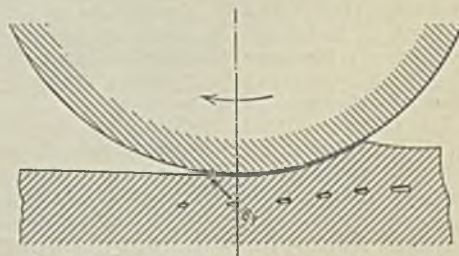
Zusammenschweißen der Gasblasen.
